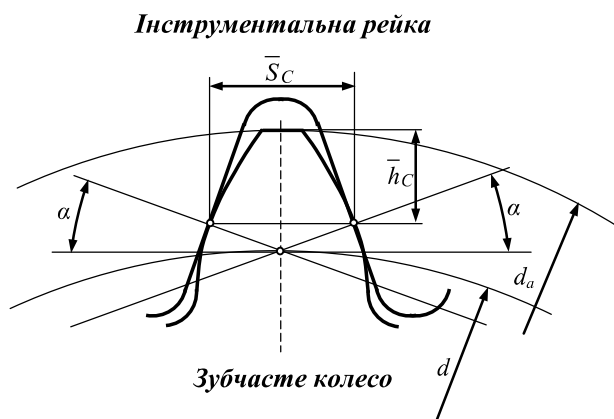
Схема вимірювання постійної хорди для зубчастих коліс із зовнішніми зубцями
